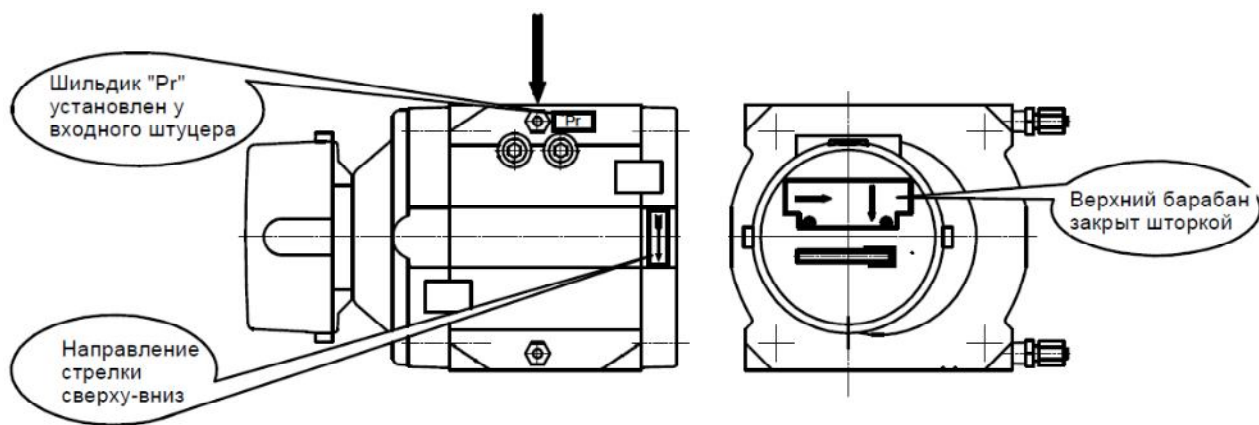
Установка шторки и шильдиков при направлении потока газа сверху-вниз. Счетная голова повернута на 90°
